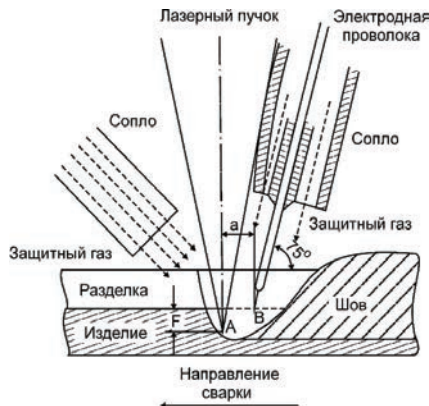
Гибридные лазерно - дуговые процессы сварки
